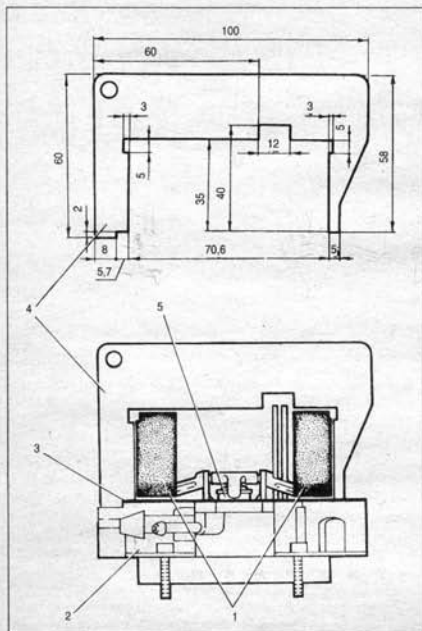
Установка уровня топлива в поплавковой камере: 1 - поплавок; 2 - крышка карбюратора; 3 - прокладка; 4 - калибр для проверки положения поплавков; 5 - игольчатый клапан
